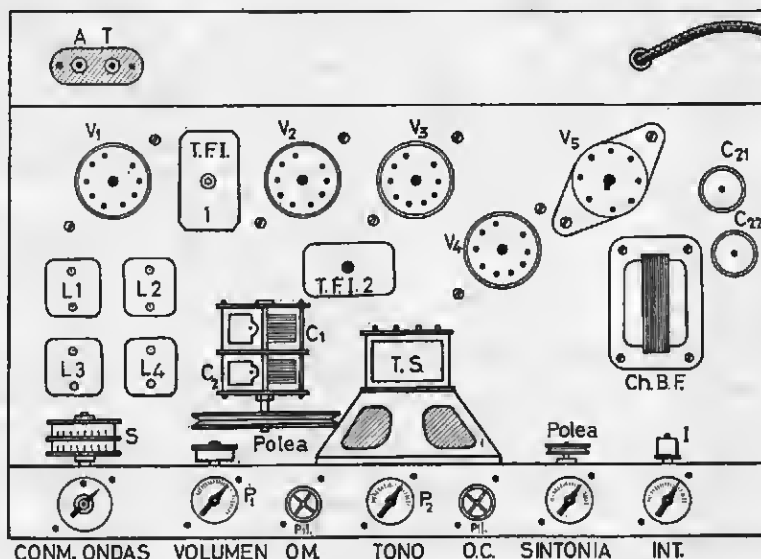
Disposición de los elementos en la parte superior del chasis.
